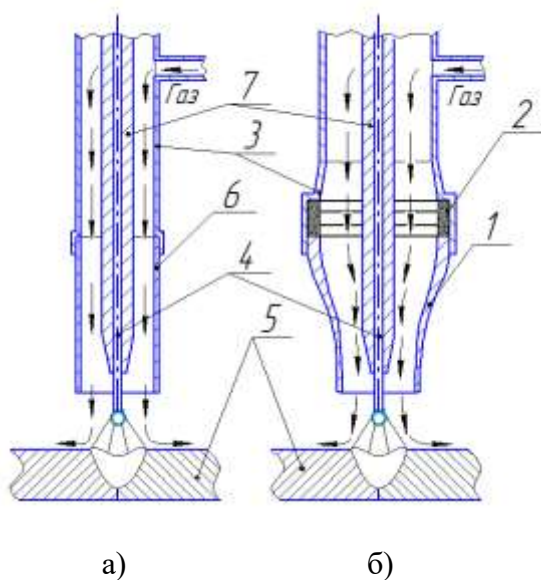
Схема различных сварочных сопел:
